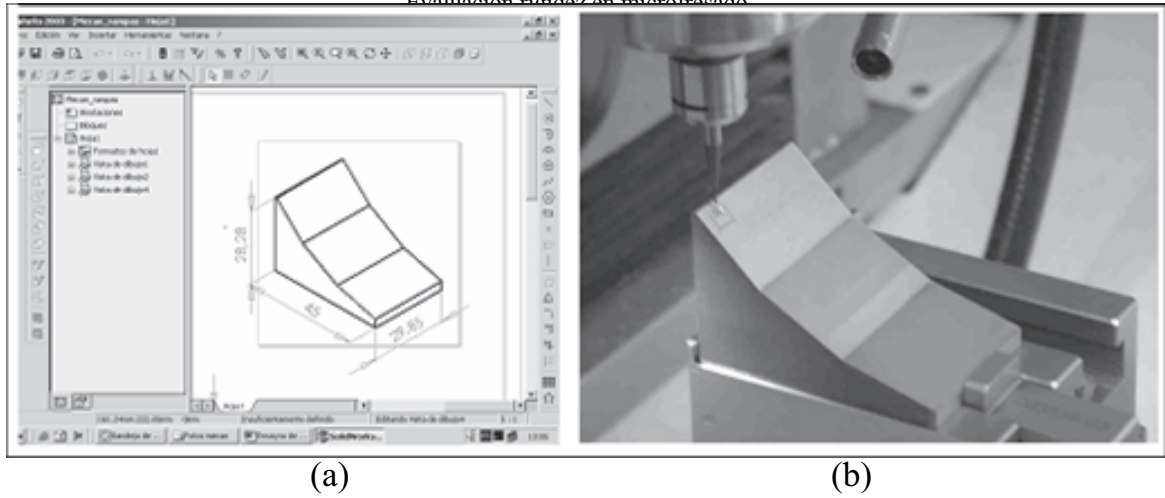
Ensayos de mecanizado para verificar la flexión de la herramienta durante el mecanizado: a) diseño CAD de la pieza; b) mecanizado en ULPRE II.
